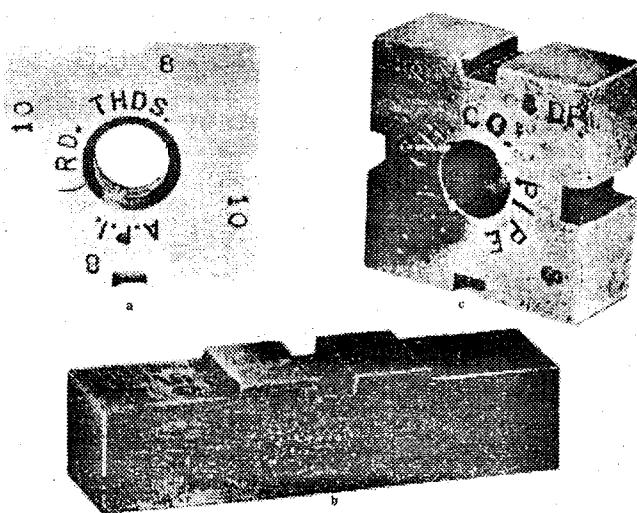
Установочные эталоны для (а) резьбы круглого и V-образного типа по API, (б) трапециевидной резьбы безмутфовых соединений и 16-дюймовой и больше и (с) установочный эталон в виде V-образного блока для контактной и точечной проверки.
